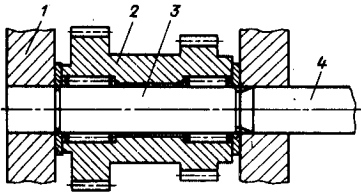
Монтаж шестерни на игольчатых подшипниках
